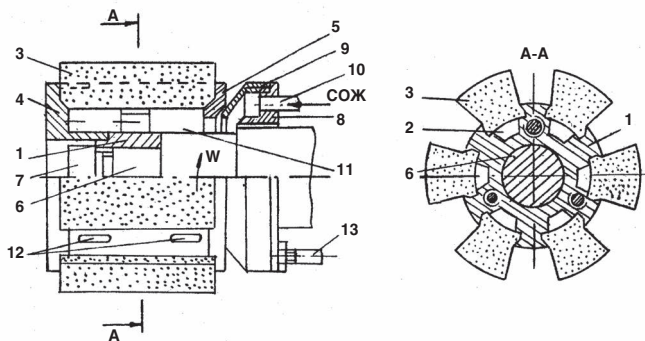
Конструкция сборного абразивного круга с прерывистой режущей поверхностью и устройством для подачи СОЖ: 1 — корпус; 2 — паз корпуса; 3 — абразивный сегмент; 4, 5 — крышки; 6 — шпиндель; 7 — болт; 8 — фланец; 9 — коническая гайка; 10 — трубопровод; 11 — полость инструмента; 12 — продольные щели; 13 — стержень.
